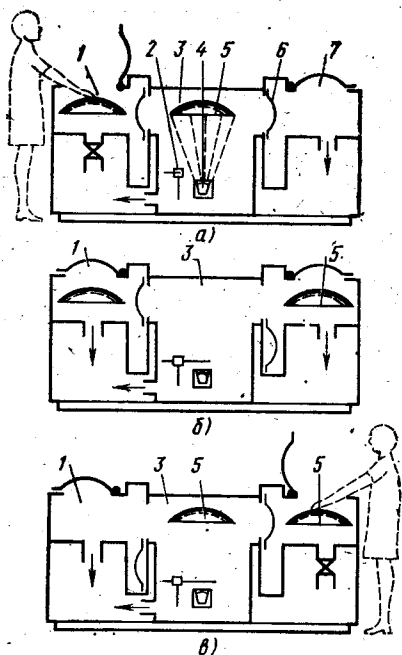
Установка полунепрерывного действия линейной компоновки с двумя шлюзовыми камерами:
